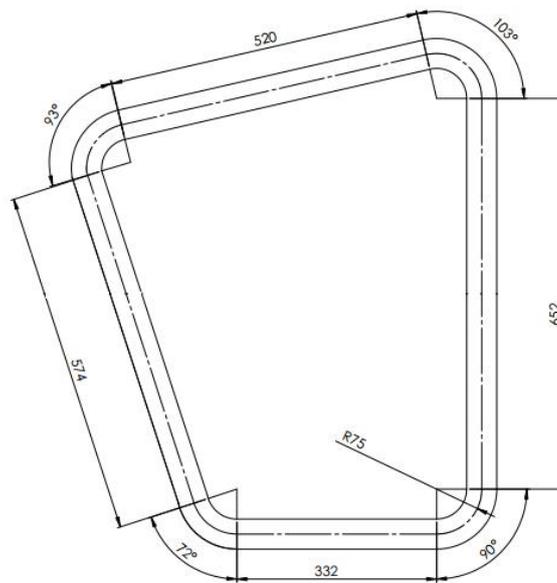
Dimensiones de la pieza Tubo Apoyo.
